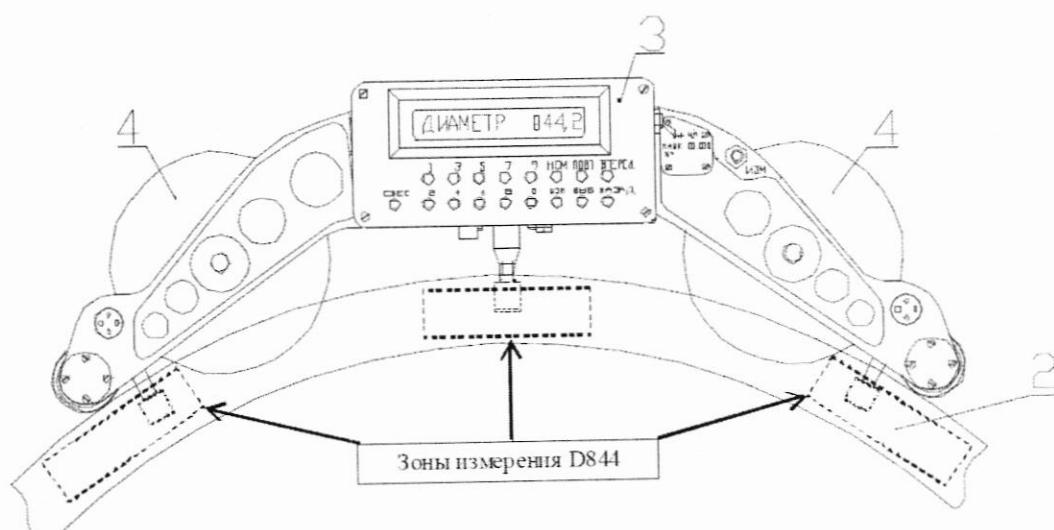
Установка прибора на приспособление для поверки ПП-МАИК.01.000 без концевых мер длины.
